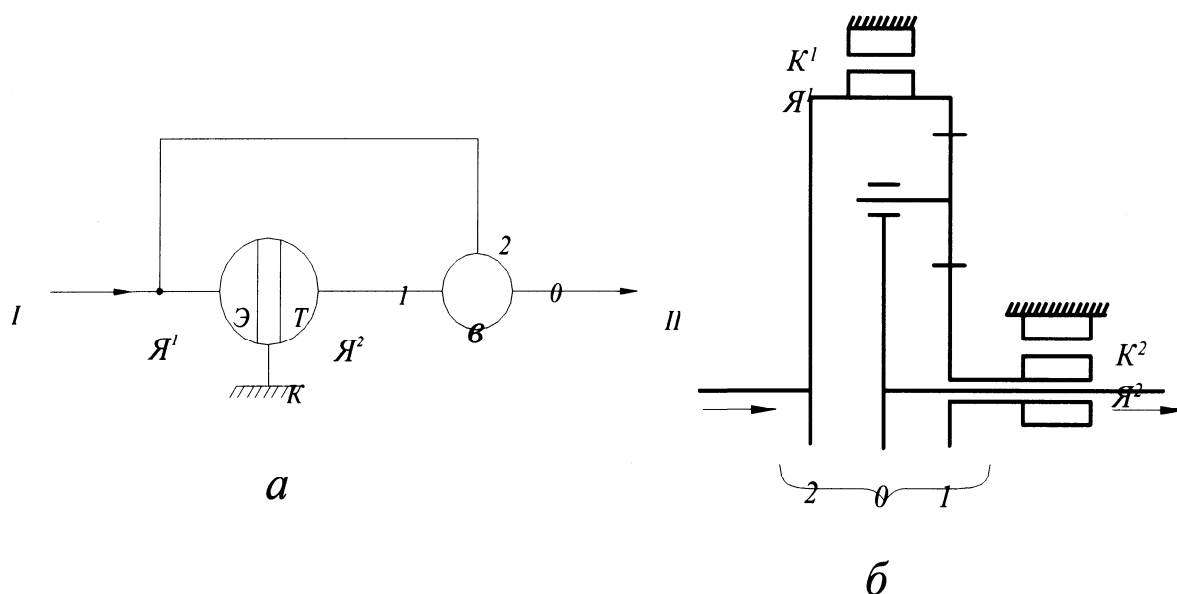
Схема силового потока (а) и кинематическая схема (б) передачи АСФ
